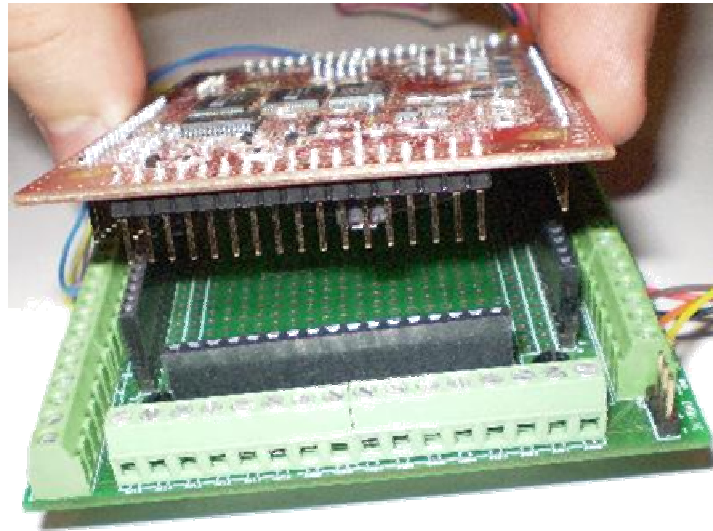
Acoplagem da LP3500 com a placa de prototipagem
